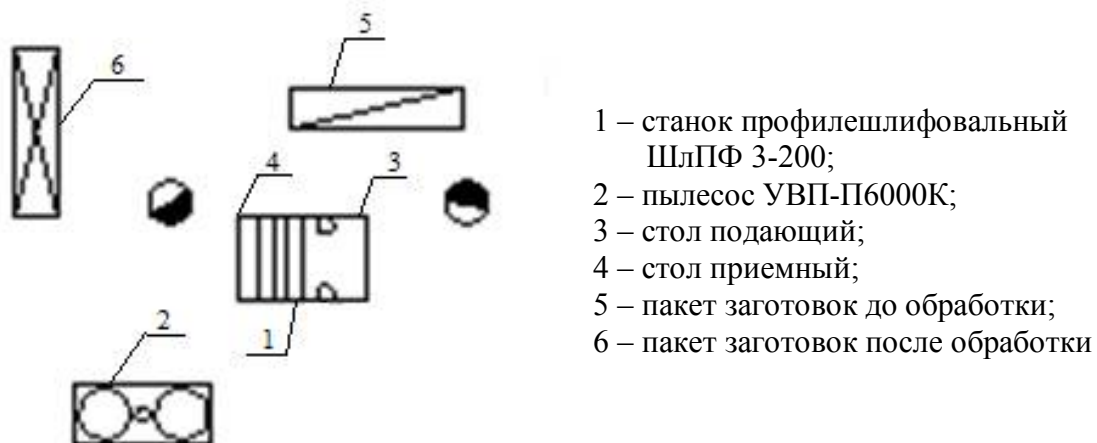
План рабочего места у профилешлифовального станка ШлПФ 3-200
